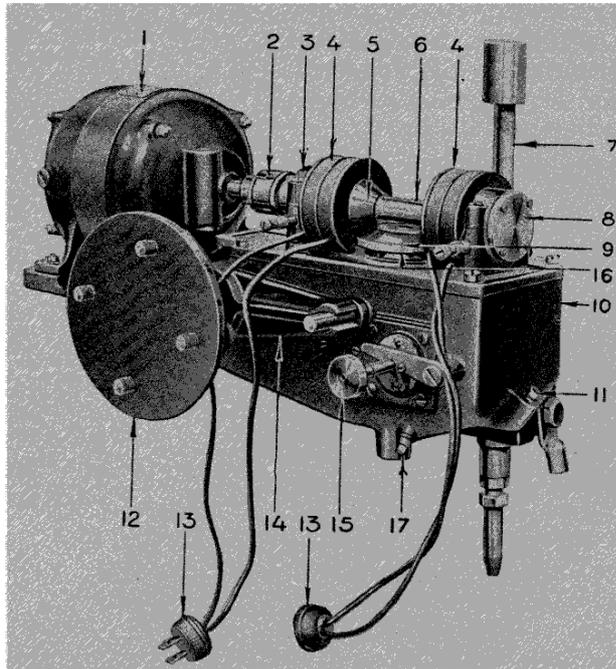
Vue de la tête de soudure automatique montrant l'embrayage magnétique.
